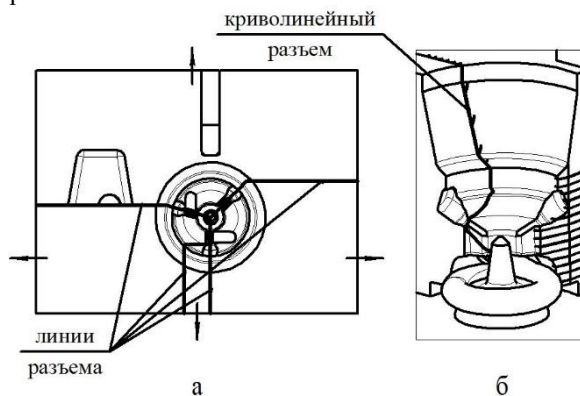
а - Схема расположения линий разреза и направления разреза, б – криволинейный разрез
